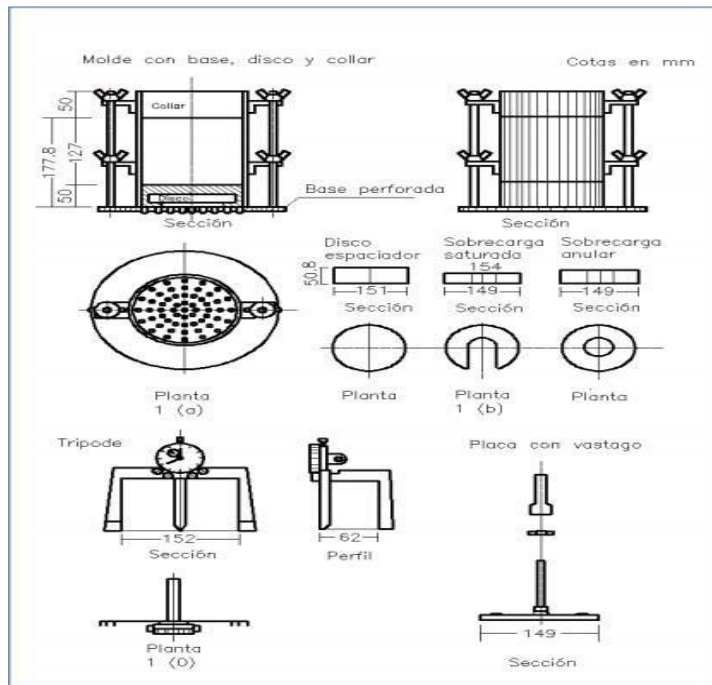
Molde de metal cilíndrico [17, p. 219]
